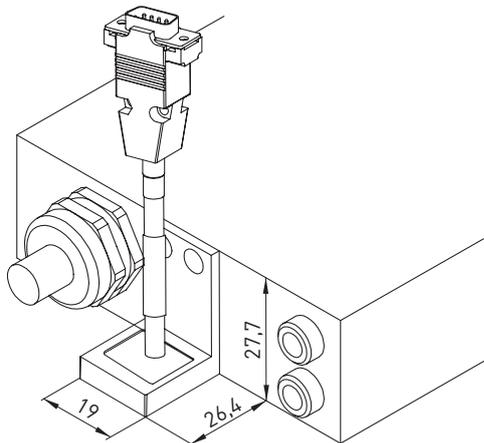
Beispielhafte Befestigung eines Hallensensors an einem LMFA-Linearmotor
